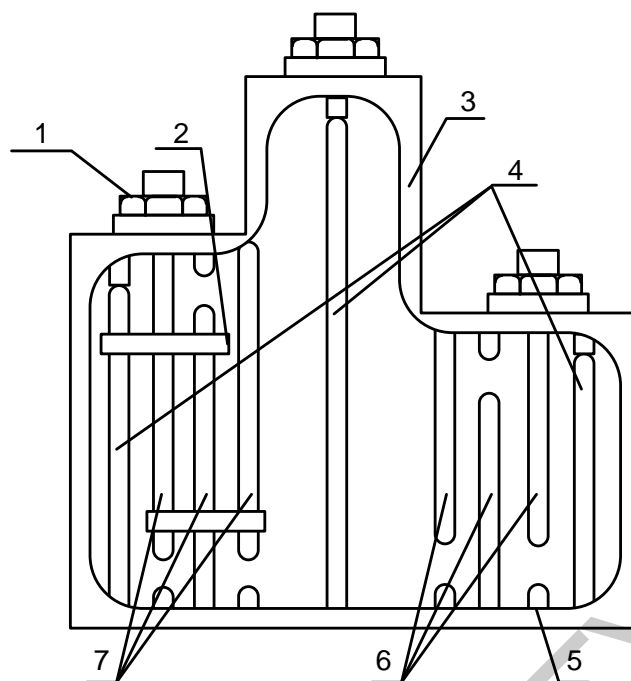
Схематический чертеж субблока совмещения каналов:
